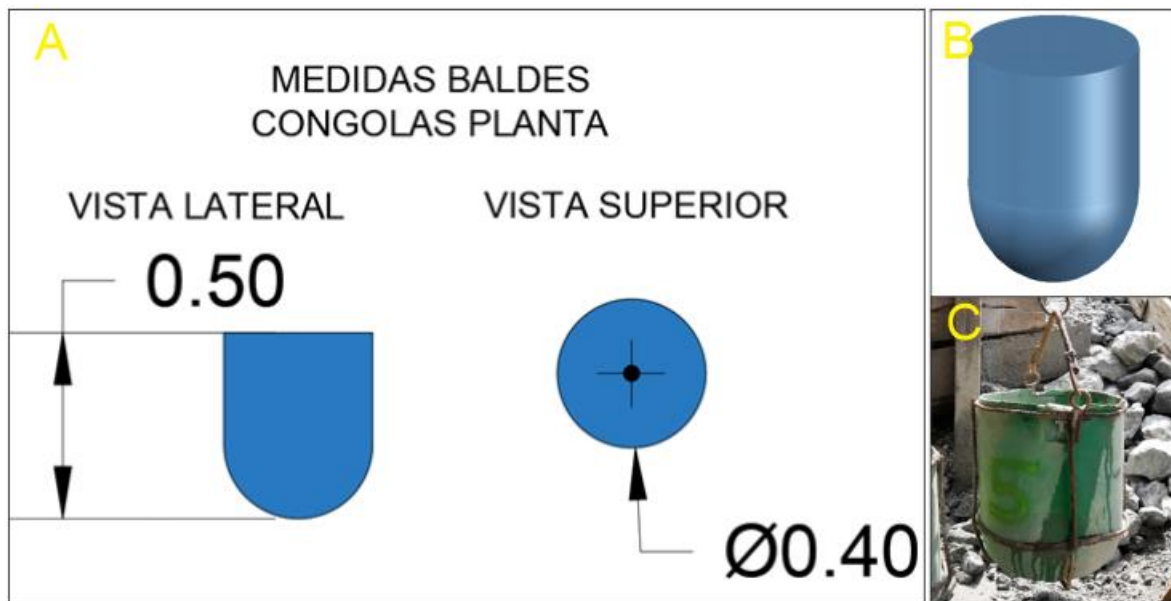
A) plano (en metros); B) modelo 3d; C) fotografía, baldes de trasporte mineral a planta.
